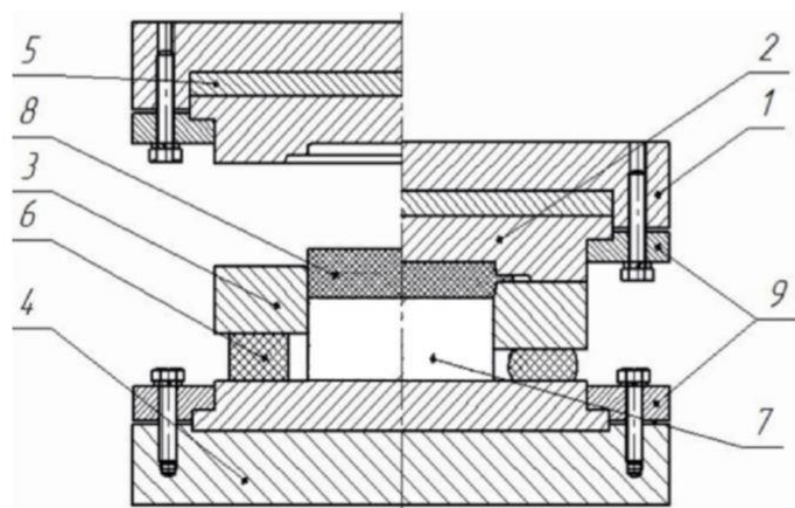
Напівзакритий штамп для гарячого штампування: 1 – верхня плита; 2 – верхня на пів матриця; 3 – нижня на пів матриця; 4 – нижня опорна плита; 5 – опорна пластина; 6 – пружний елемент; 7 – нижній пуансон; 8 – заготовка під штампування; 9 – верхній і нижній кріпильні фланці
